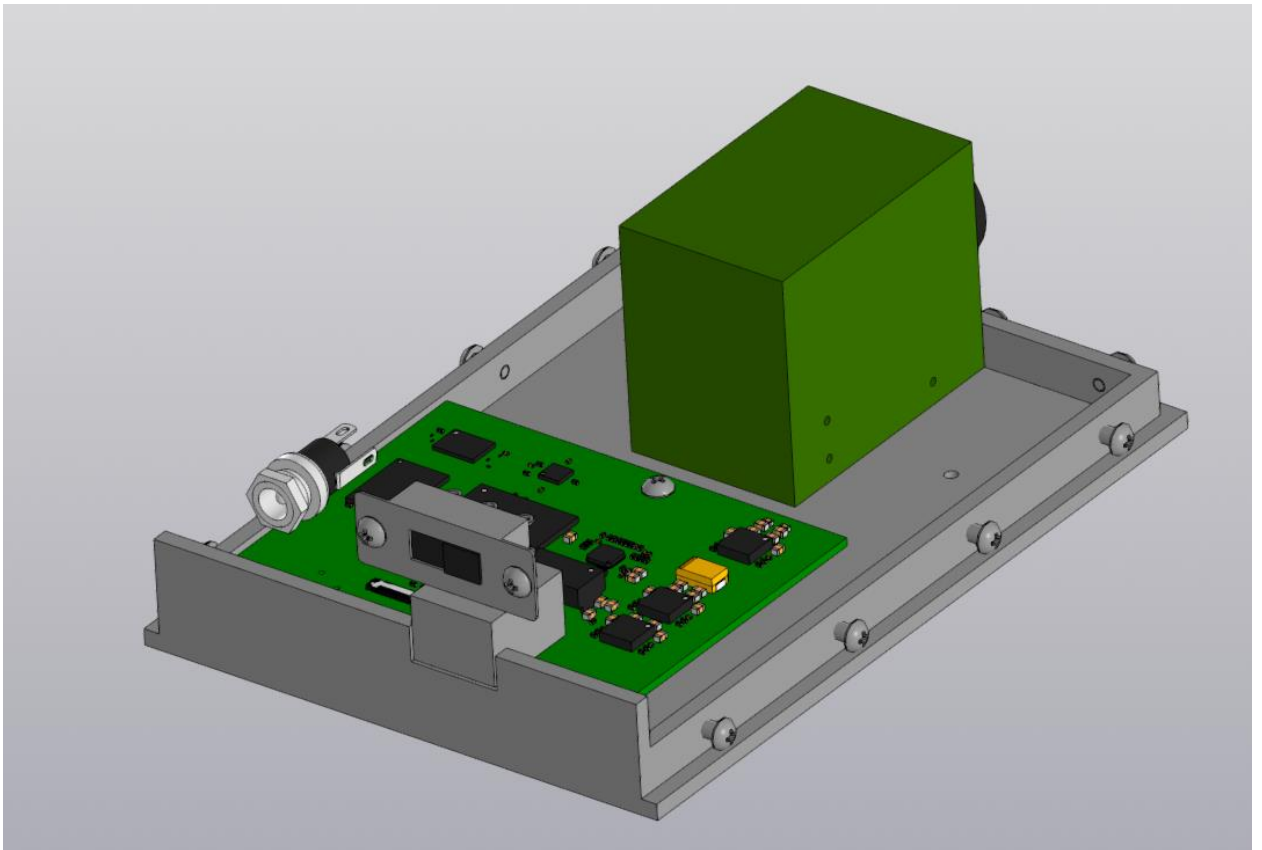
3D-изображение общей сборки: вид сверху сзади, без крышки
